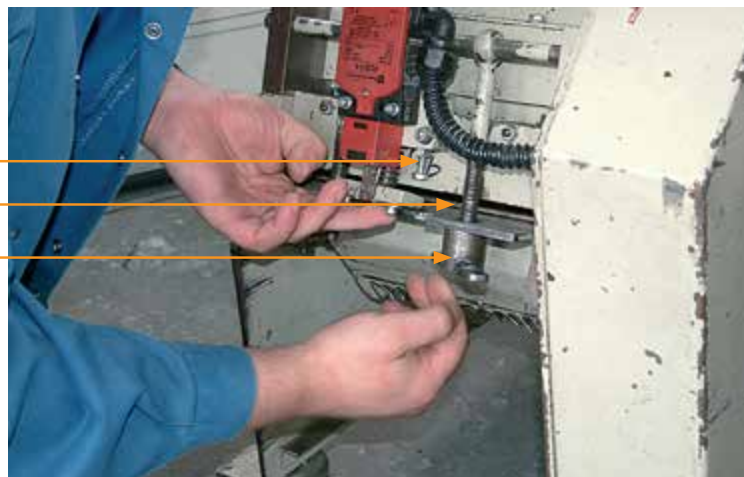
Leicht manipulierbare mechanische Nachlaufüberbrückung an einer Zerkleinerungsmaschine
